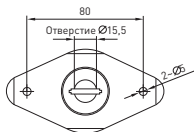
Отверстия для монтажа на фланец ТНТ-102
